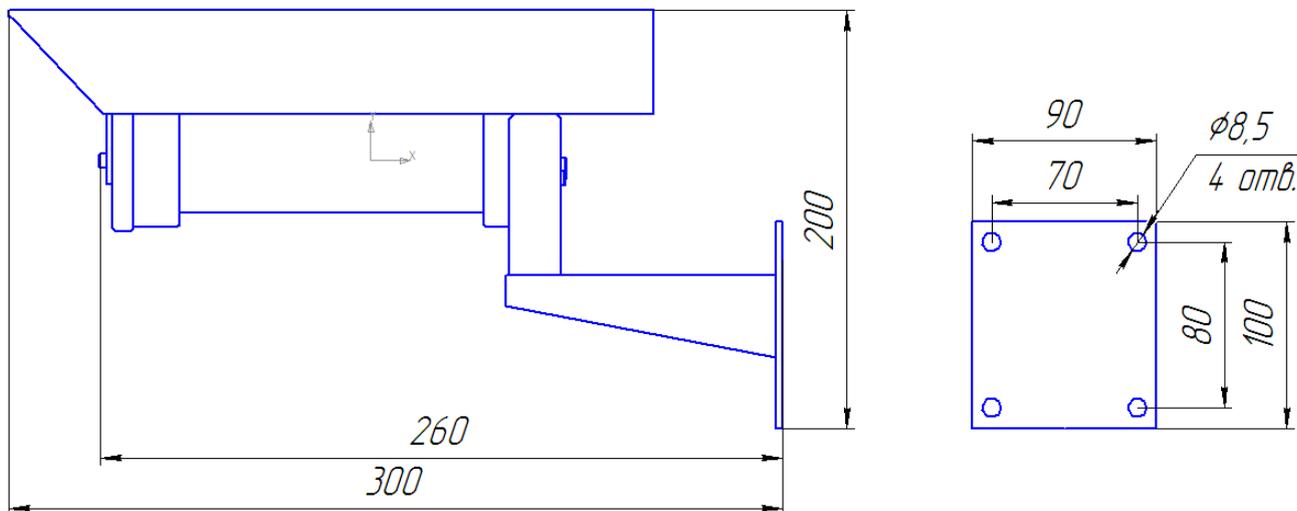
Габаритные размеры извещателя с крепежно-юстировочным устройством
